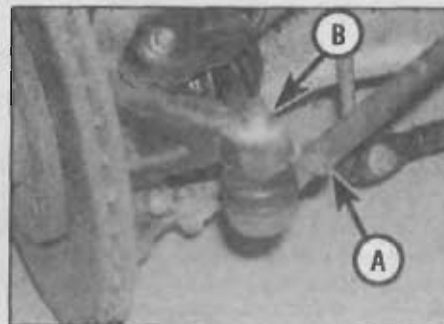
Расположение контргайки (А) шарового шарнира наконечника рулевой тяги и гайки (В) крепления шарового шарнира к поворотному кулаку.
